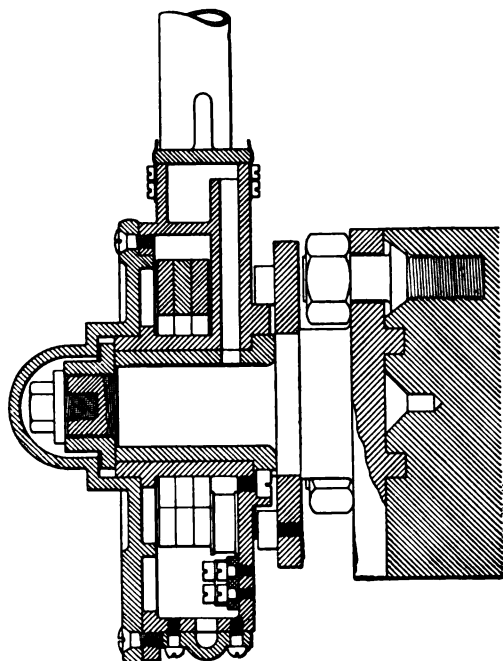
Lokomotivgeber, Innenansicht und Schnitt.
